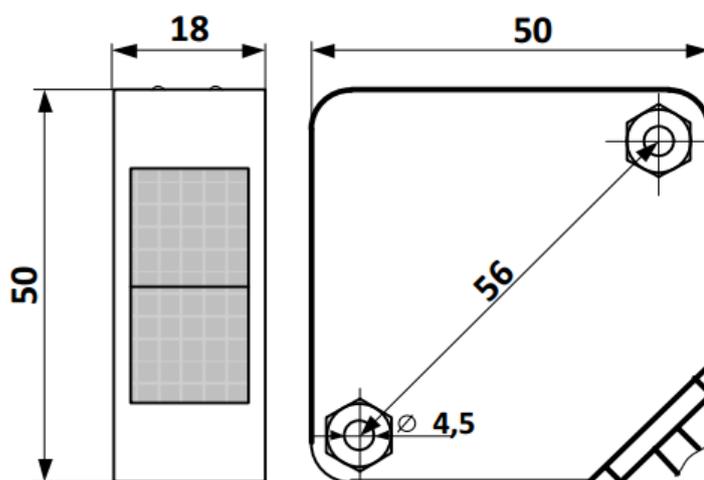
Габаритные размеры барьерного датчика ВИКО-Б-109-ПЗ [9]
